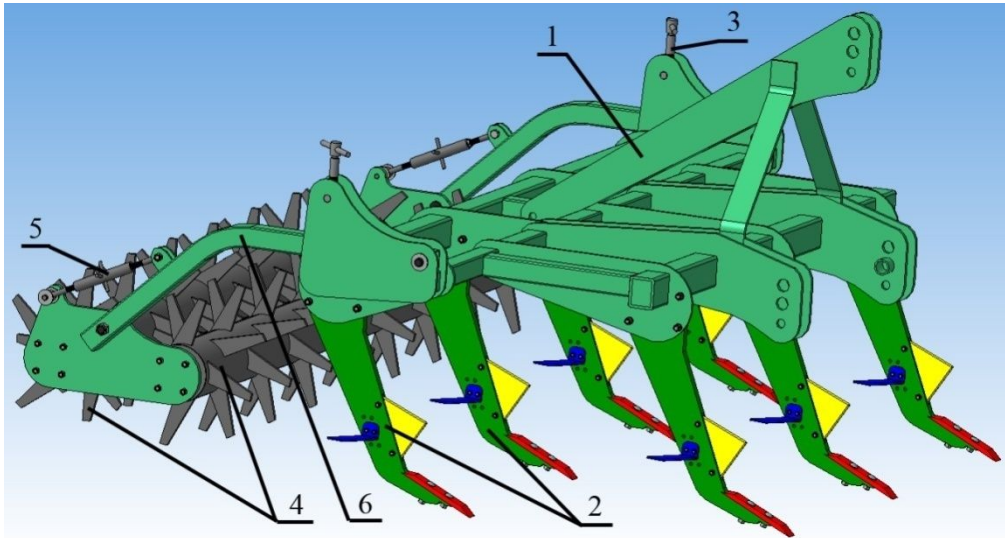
Загальний вигляд комбінованого чизеля: 1 – рама; 2 – лапа чизельна; 3 – регулювальний механізм; 4 – спарений зубчастий коток; 5 – гвинт; 6 – механізм кріплення котка
